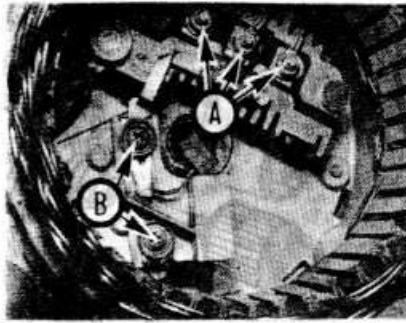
Гайки крепления провода статора (А) и винты держателя щеток/регулятора напряжения (В) — генератор тока Delco-Remy
